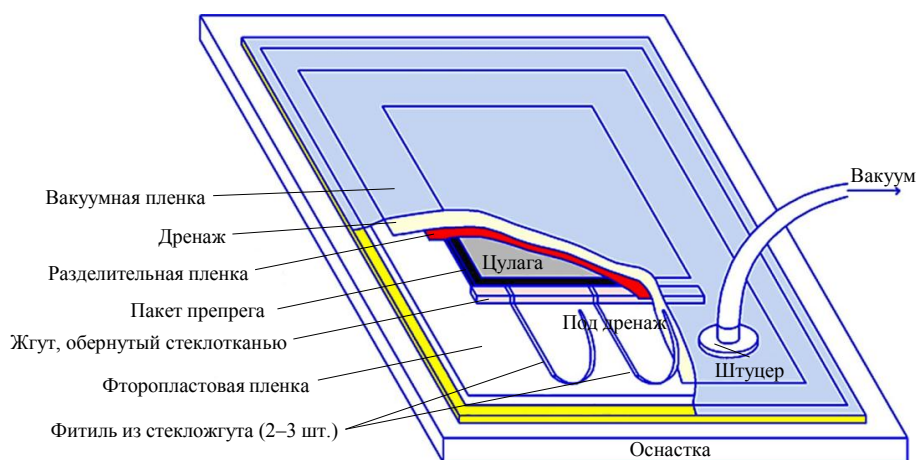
Схема сборки пакета-заготовки для изготовления монолитных плит из углепластика
